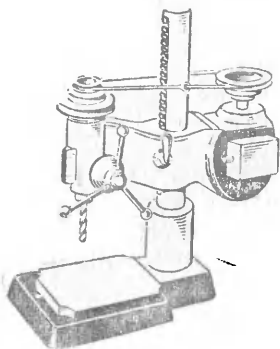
Ременная передача у станка. Перемещение ремня с одного шкива на другой позволяет менять число оборотов.
